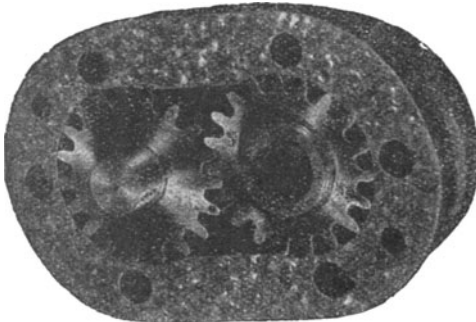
Ölpumpe für die Druckölschmierung der Dampfturbinenlager.
